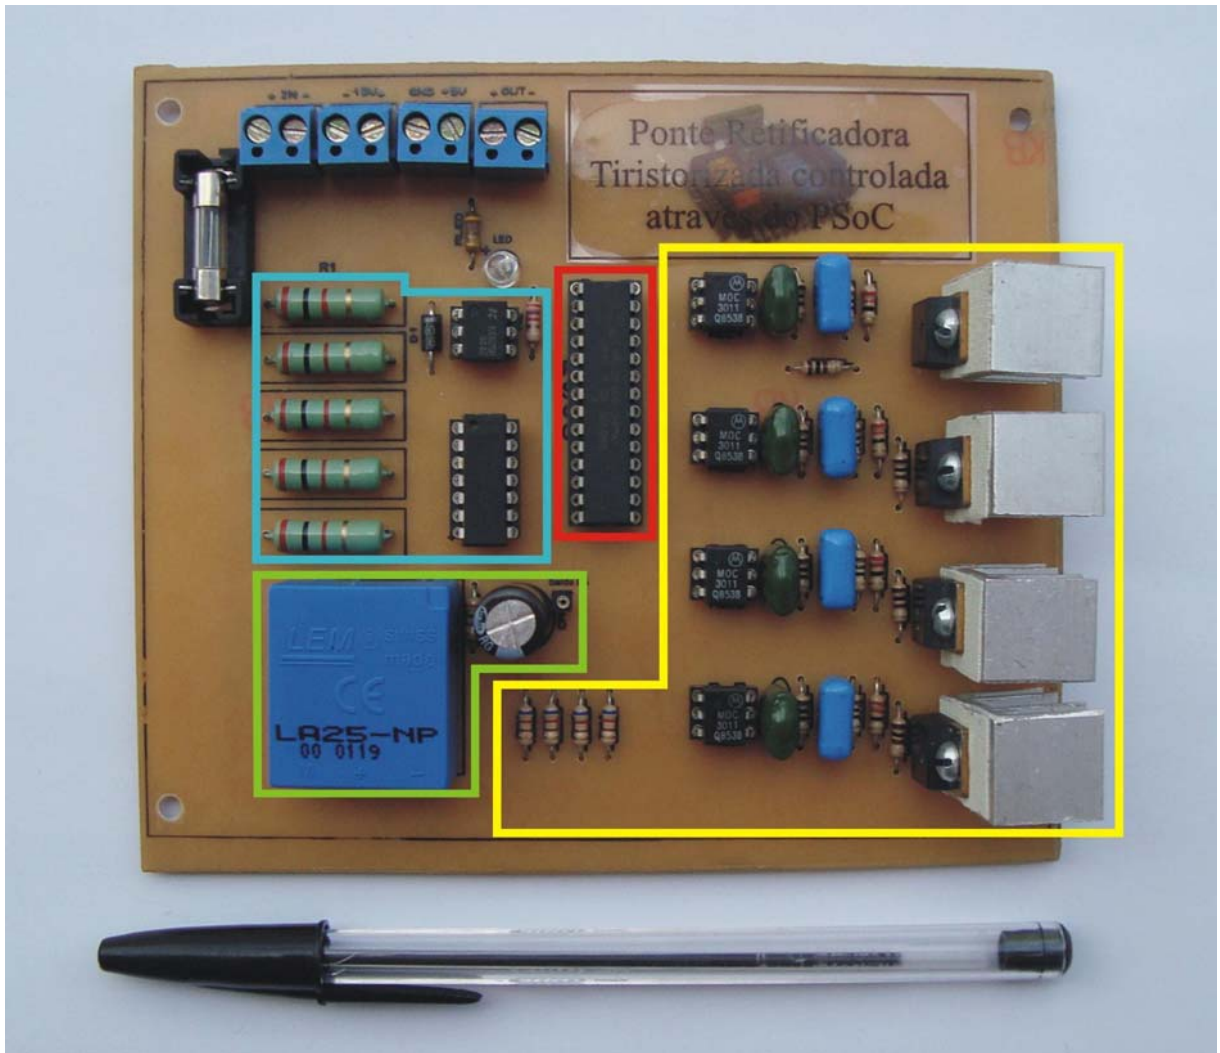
Aspecto final da placa de circuito impresso.
